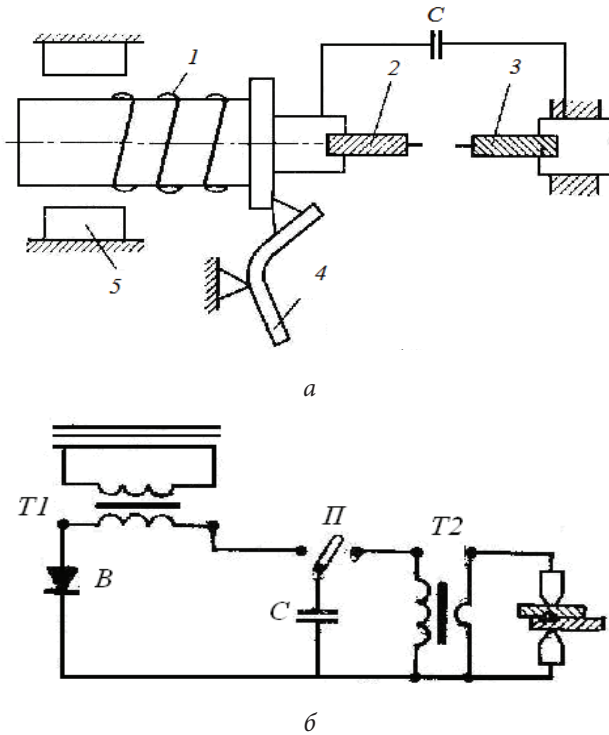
Схемы конденсаторной сварки: а — с подачей тока непосредственно от конденсатора на свариваемые заготовки (1 — пружина; 2, 3 — свариваемые заготовки; 4 — защелка; 5 — направляющие; В — выпрямитель, П — переключатель, С — конденсаторная батарея); б — с подачей тока от конденсатора на первичную обмотку сварочного конденсатора (Т1 — повышающий трансформатор, Т2 — сварочный трансформатор)
